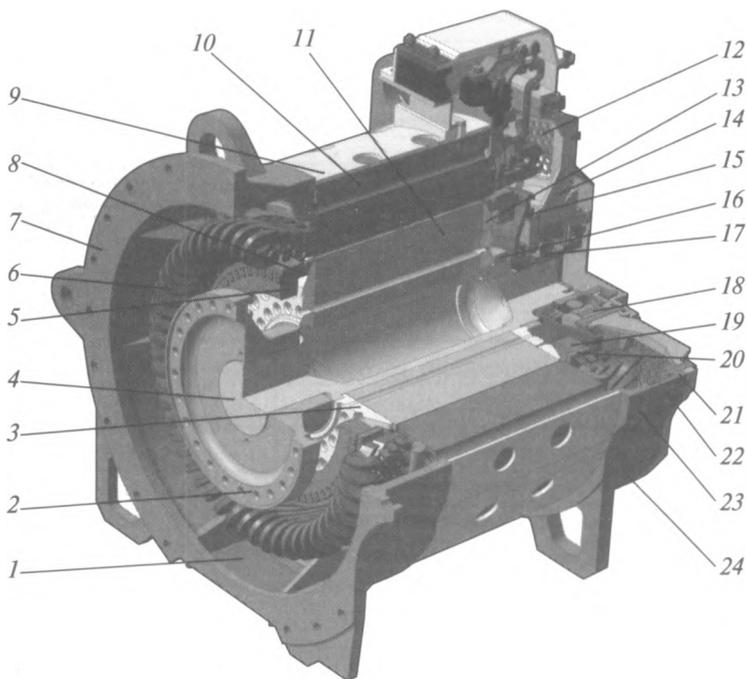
Тяговый двигатель ДТА-1200А в разрезе:
